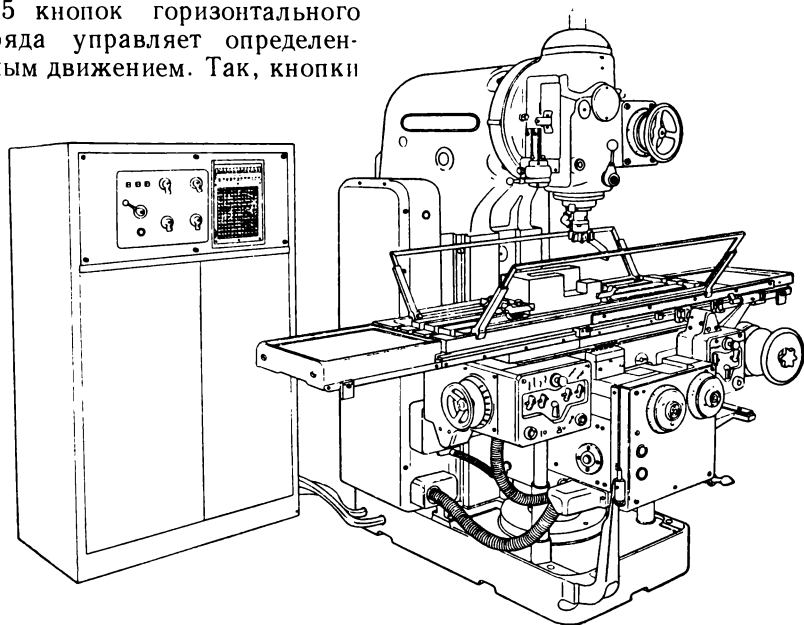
Консольный вертикально-фрезерный станок мод. фирмы Ф. Вернер
